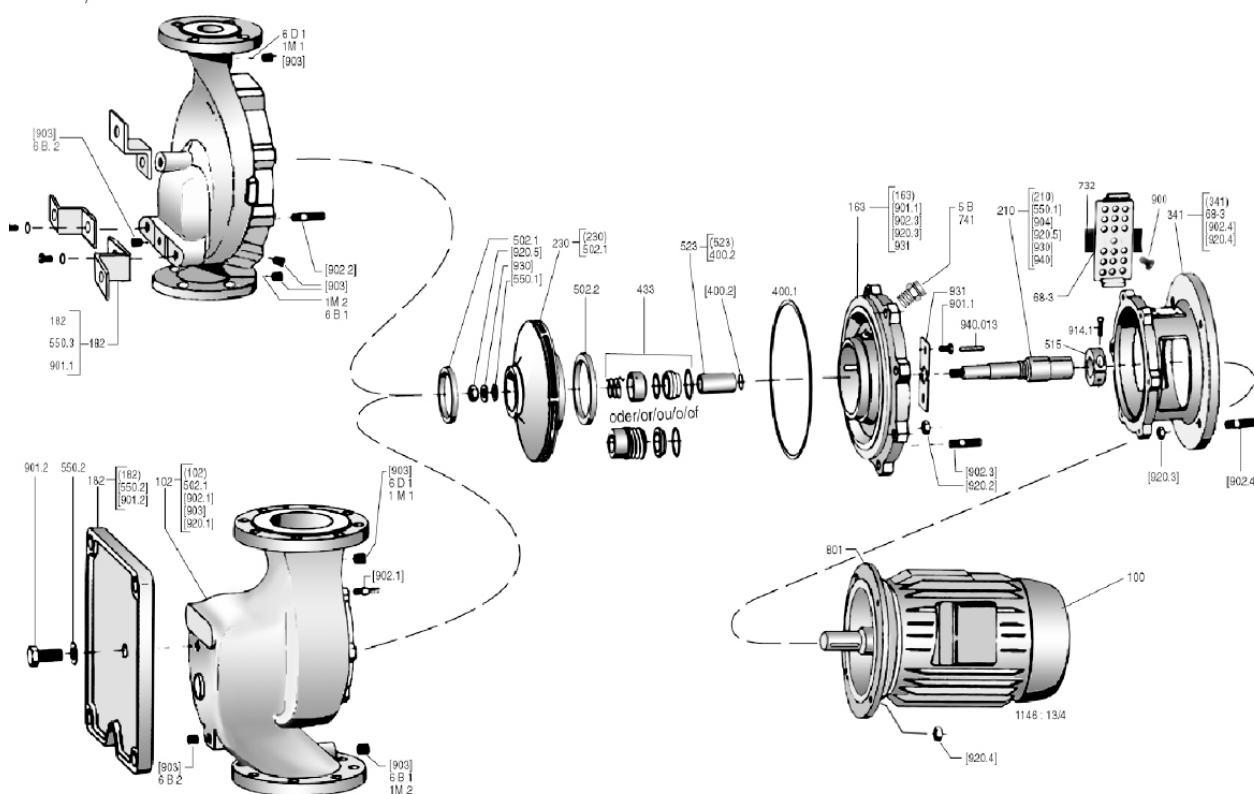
Стандартное торцевое уплотнение и резьбовая напорная крышка
